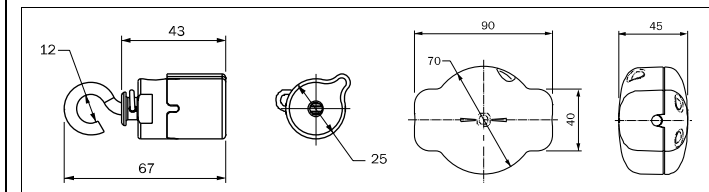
Dibujo acotado de las abrazaderas y el rodillo tensor
